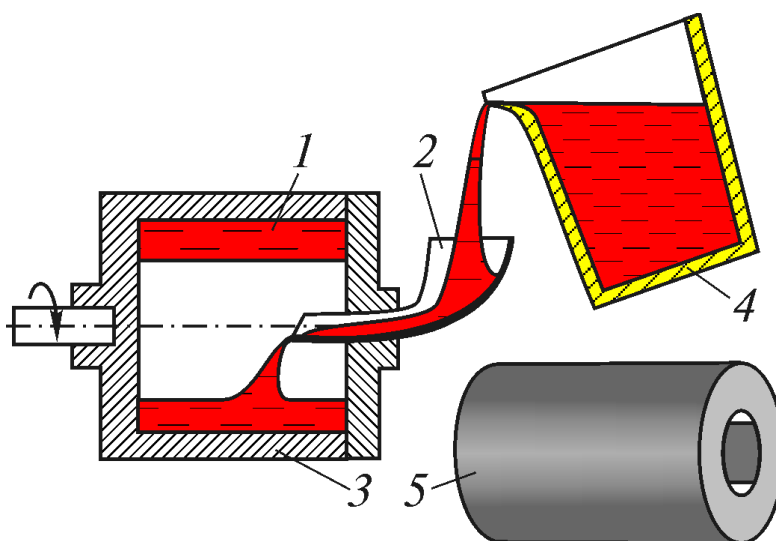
Схема відцентрового лиття порожнистих циліндричних заготовок в машині з горизонтальною віссю обертання: 1 - розплав; 2 - жолоб; 3 - виливниця, що обертається; 4 - ківш з металом; 5 – виливок
